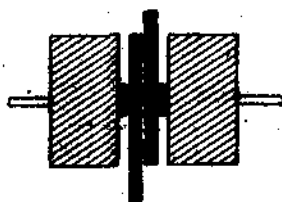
Сварка точками толстого материала (с прокладкой).
